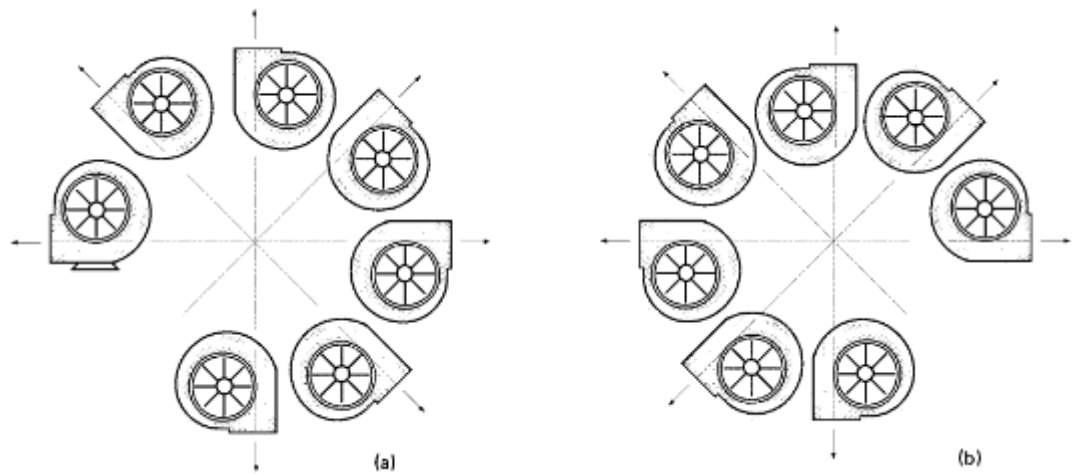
Posiciones de la boca de salida del ventilador. A) derechas. B) izquierdas.
